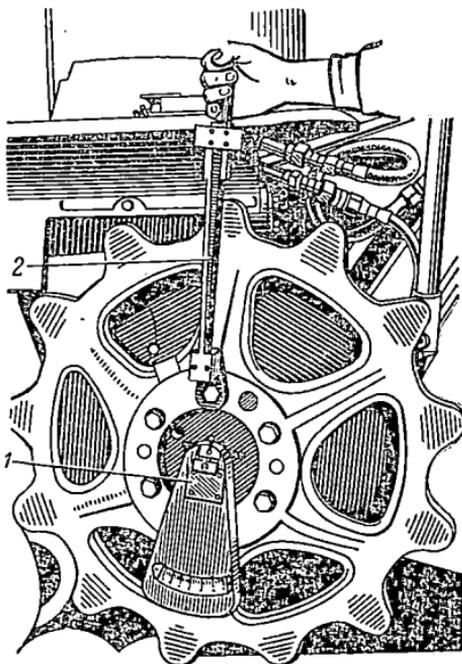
Проверка суммарного бокового зазора в механизмах силовой передачи люфтомером КИ-4813:
